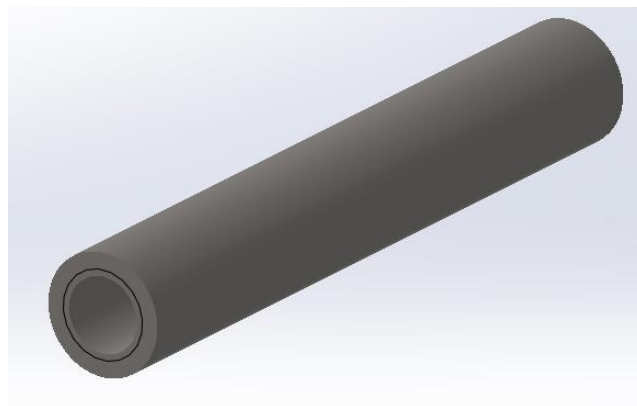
Vista de soldado de mosquetón pieza N°70 (Fuente 109)
